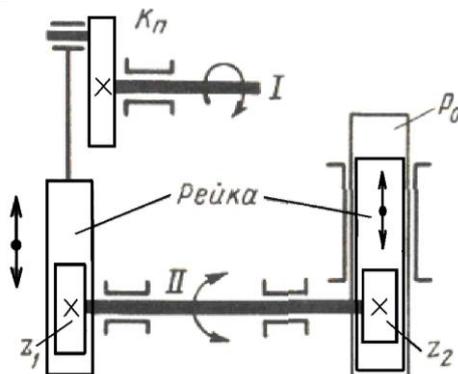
Схема двойного кривошипно-реечного механизма
